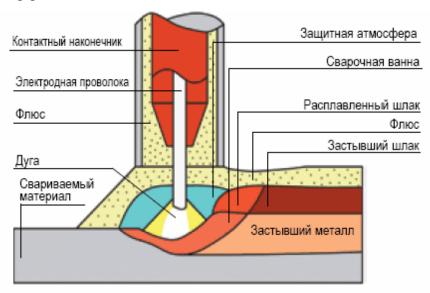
Сварка под слоем флюса[3].
